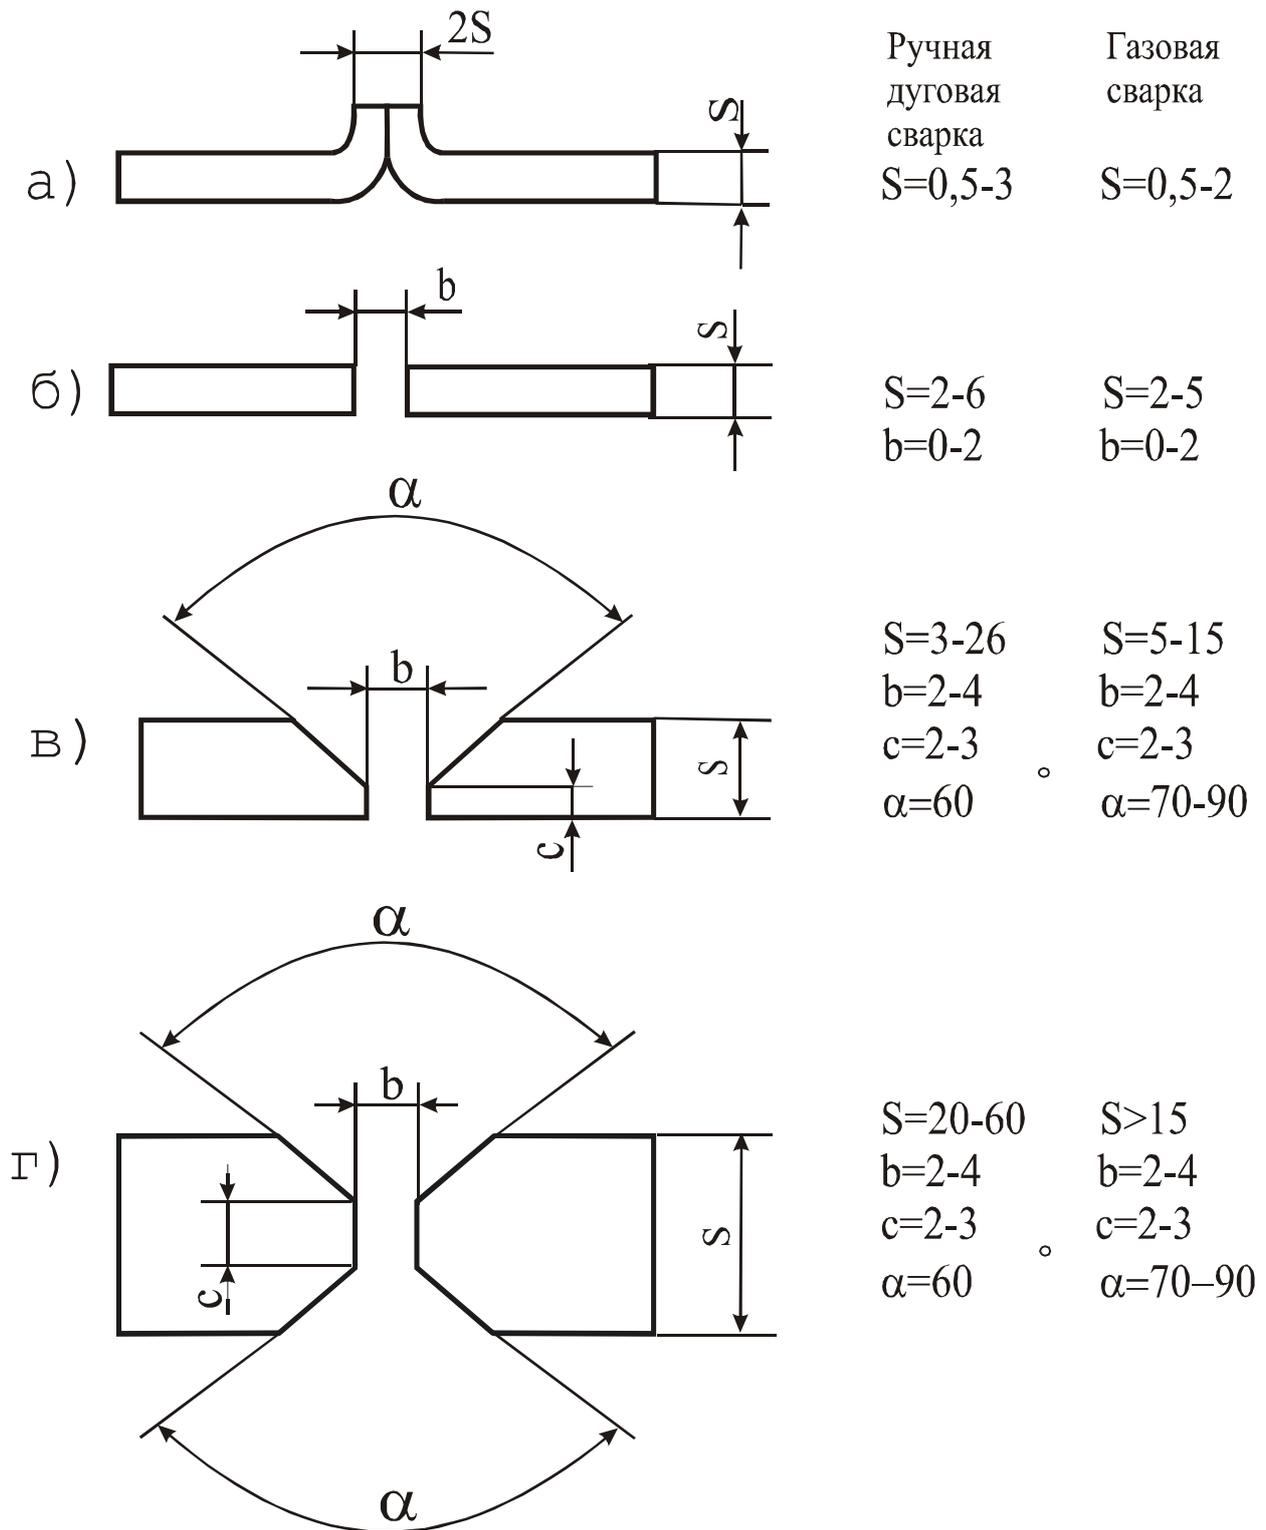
Виды стыковых сварных соединений: а) с отбортовкой кромок; б) без разделки кромок; в) с V-образной разделкой кромок; г) с X-образной разделкой кромок.
